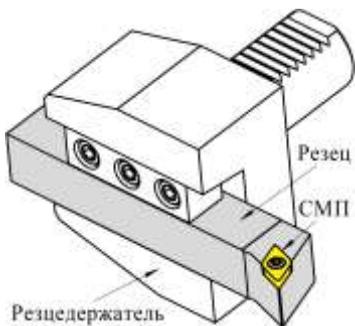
Инструментальная сборка: токарный резец в резцедержателе
